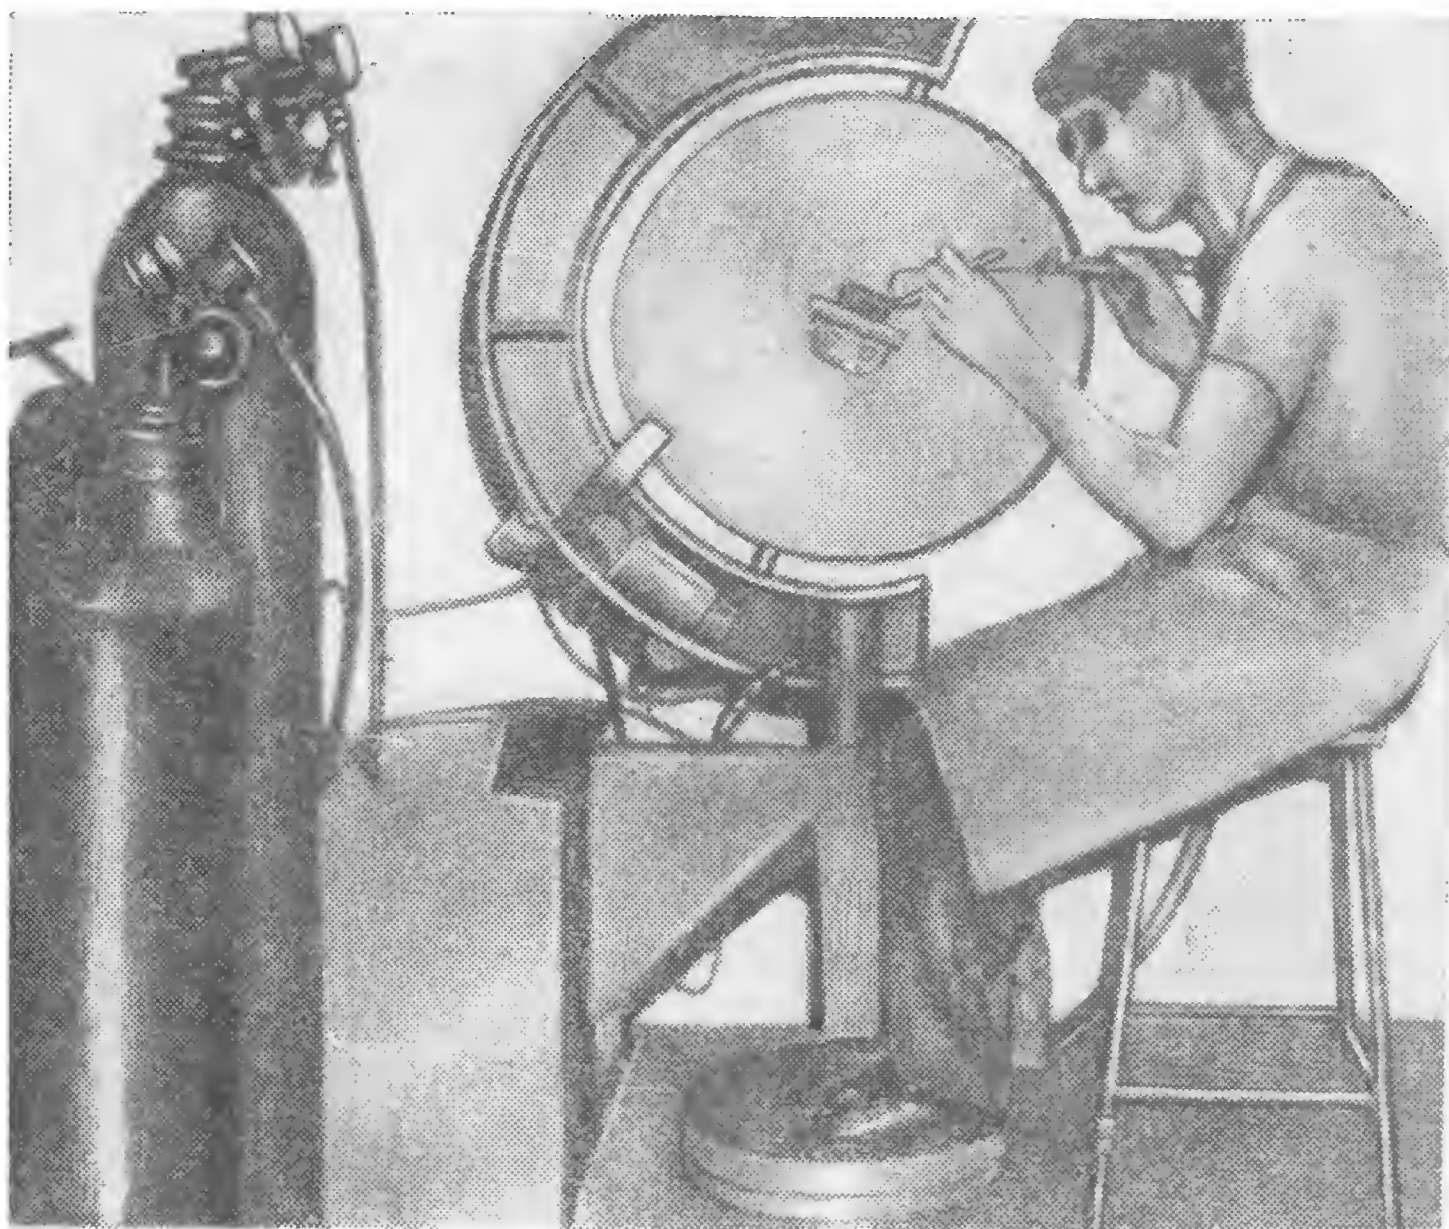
Работа на гироскопическом приспособлении для сварки мелких деталей
